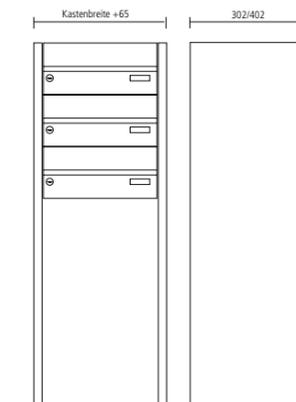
Freistehende RENZ PLAN Briefkastenanlage aus Galfan-Stahl mit Verkleidungsgestell zum Einbetonieren, geräuschgedämpfte Einwurfklappe, Tür und Einwurfklappe mit synchronem Aufklappmechanismus, RSA2-Klingelsystem und -Namensschild.
